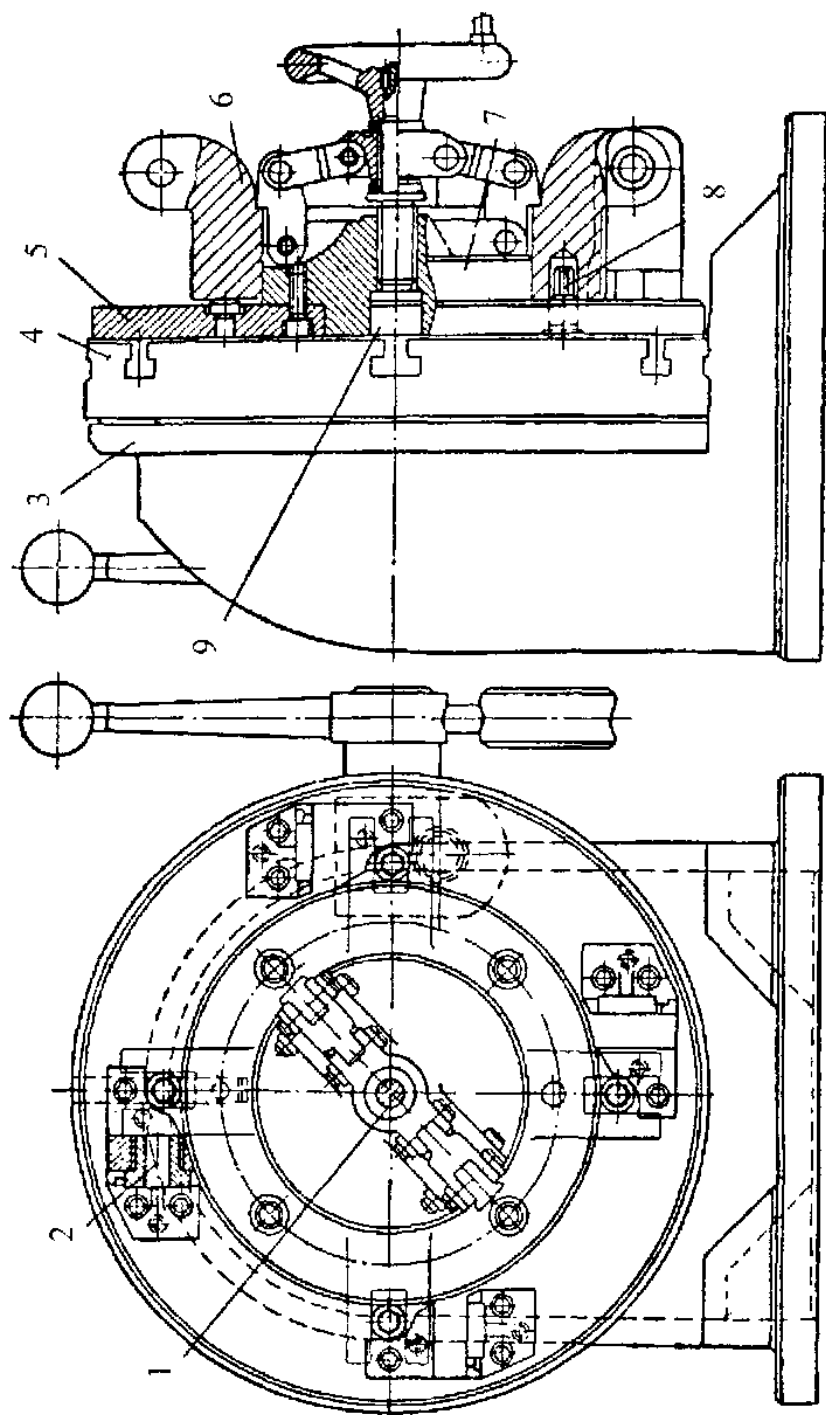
Поворотний пристрій консольного типу з горизонтальною віссю
